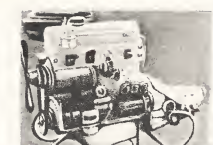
Автоматическая передача: 1 — гидравлическое пусковое сцепление, 2 — первичный масляный насос, 3, 4 и 5 — тормозная лента, 6 — задний комплект блокировки, 8 — шестерня стачнойной планетарки, 7 — ведущая шестерня регулятора и вторичного насоса, 9 — выходящий вал, 10 — второе сцепление, 11 — распределительный шит, 12 — третье сцепление, 13 — передний комплект планетарки, 14 — первое сцепление.
